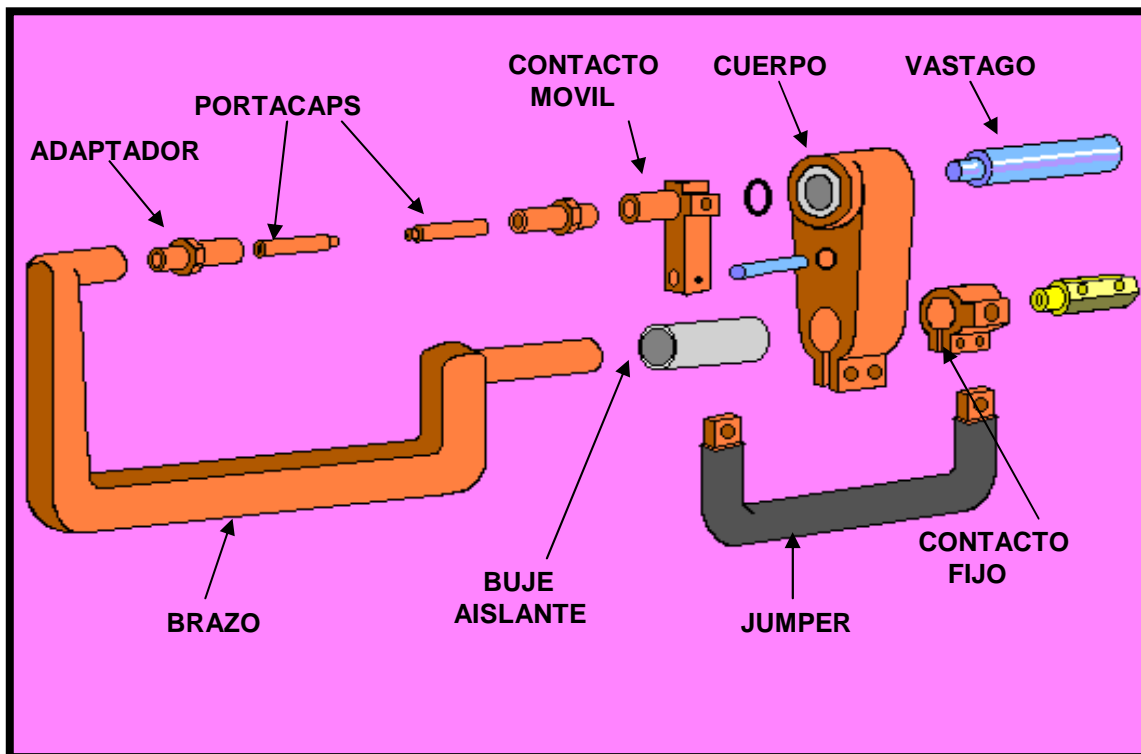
Despiece de una Soldadora Portable Tipo C.
